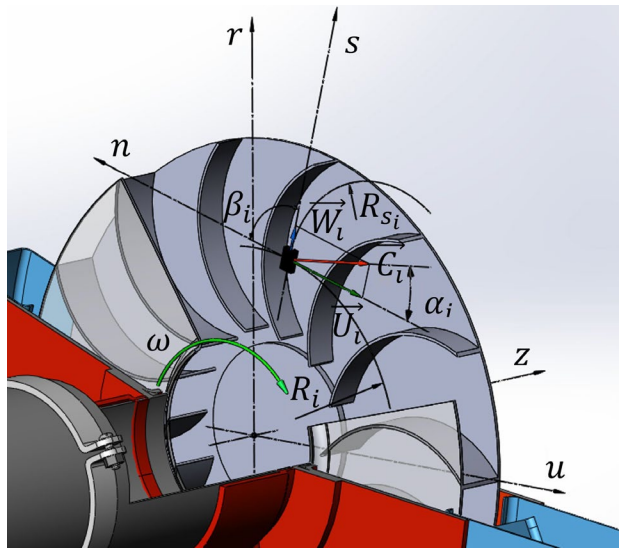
Рисунок робочого колеса вентилятора з векторами швидкості
